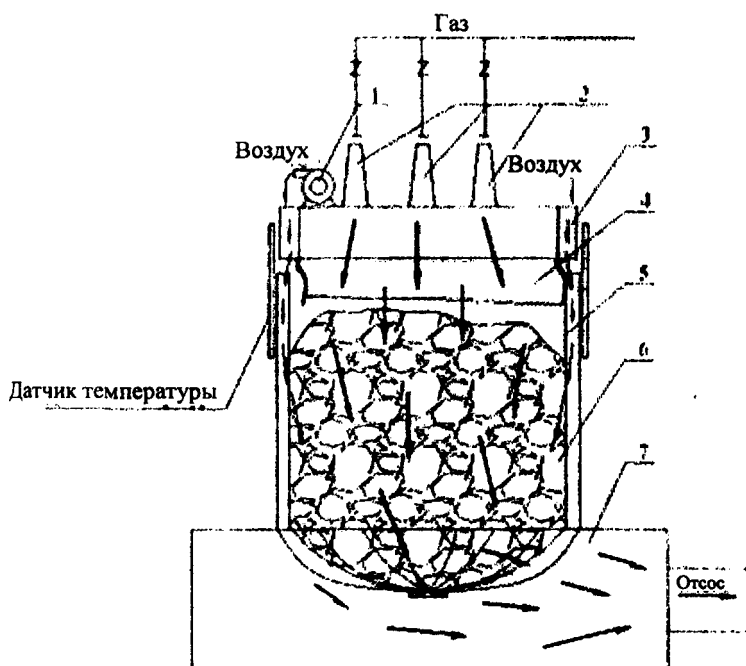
Схема работы «бадь-термоса»: 1 – продувочный вентилятор; 2 – горелки; 3 – коллектор обдува; 4 – огнестойкая завеса; 5 – вставка; 6 – нагреваемая шихта; 7 – корпус стенда
